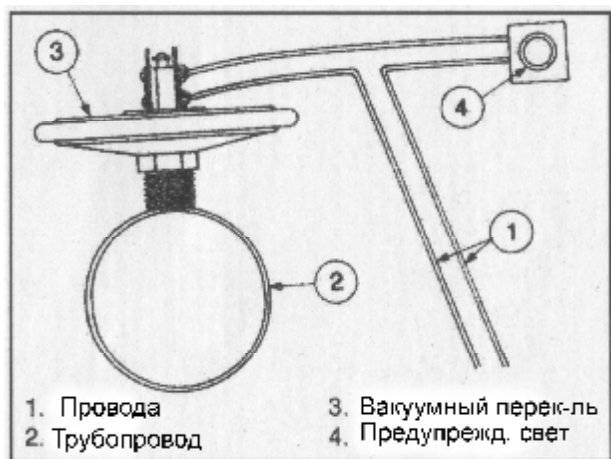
Вакуумный переключатель для проверки впуска воздуха.
